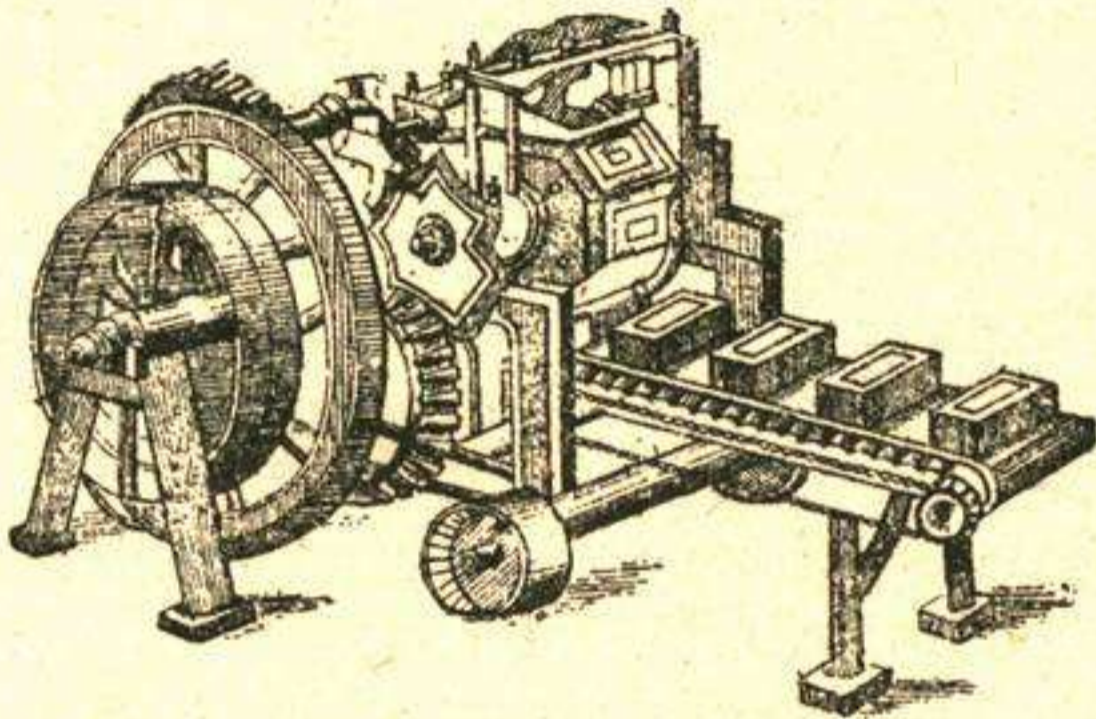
Máquina para moldear y comprimir ladrillos.
